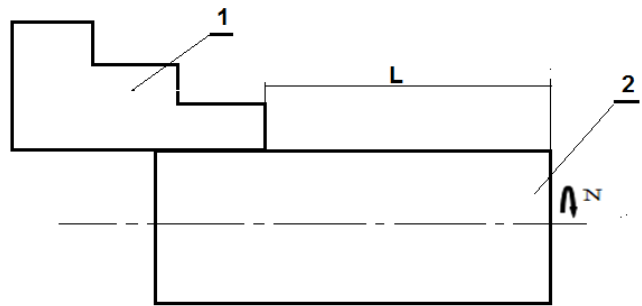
Montage de la pièce 1-mandrin, 2- pièce
